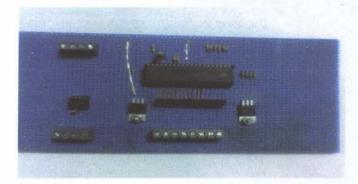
TARJETA PRINCIPAL EN PROTOBOARD.
